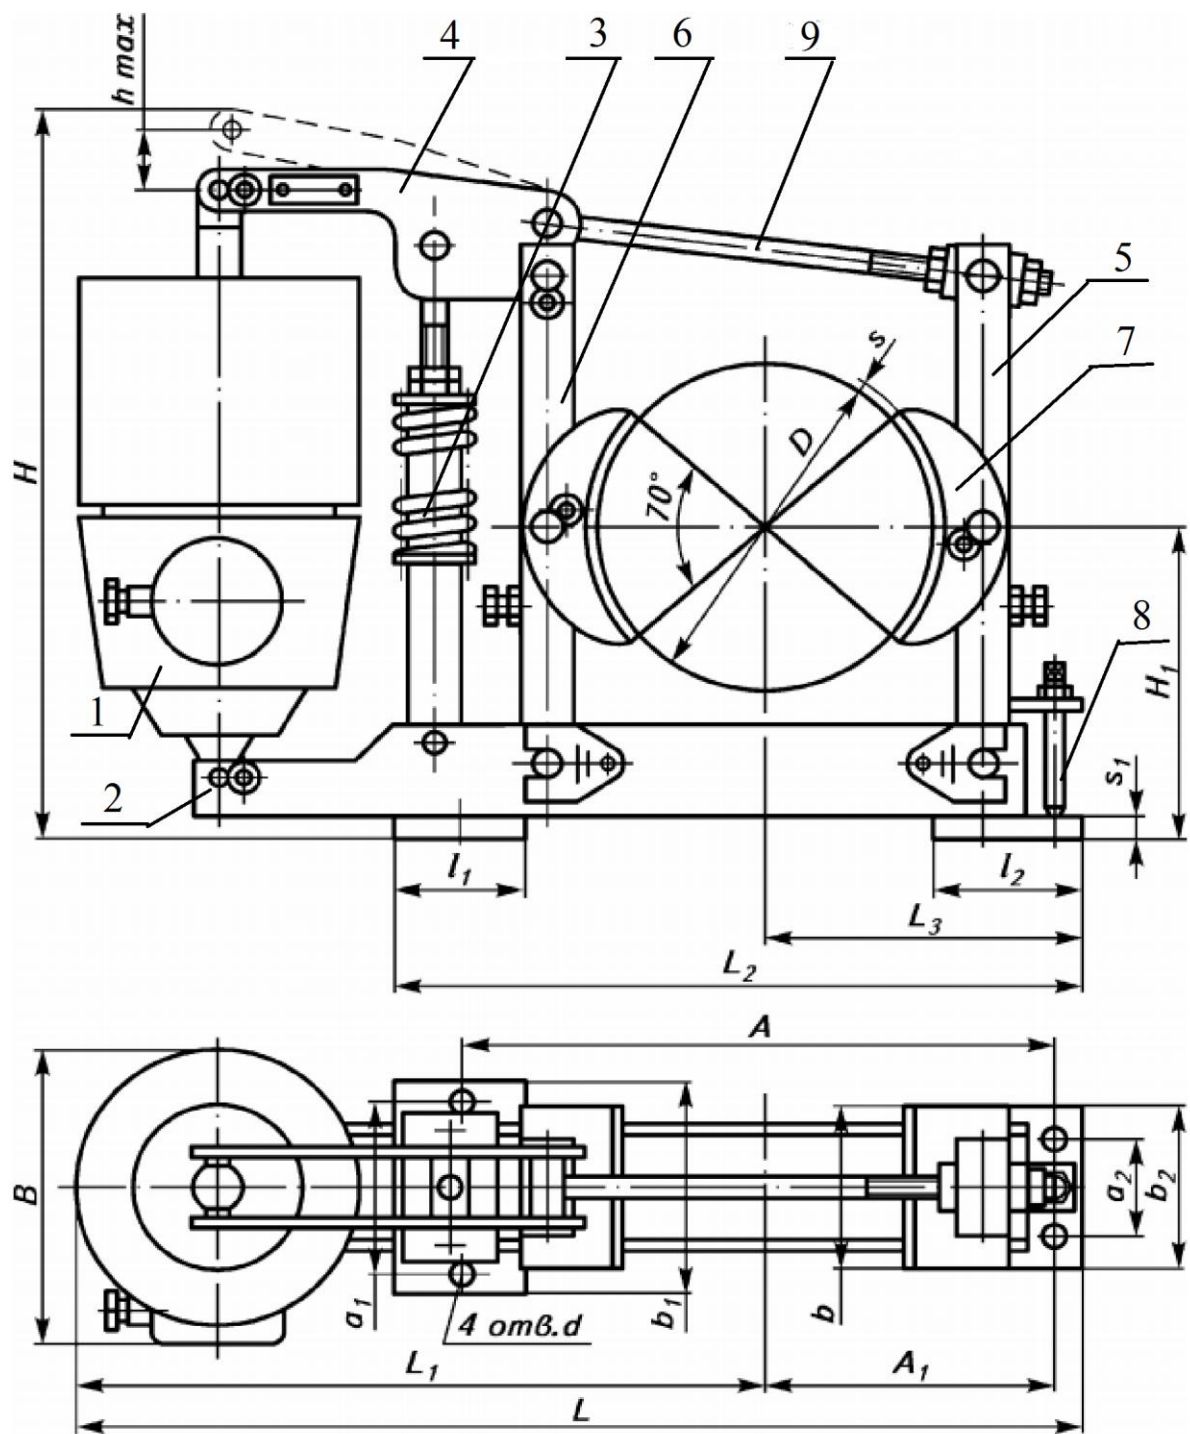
Общий вид колодочного тормоза типа ТКГ
